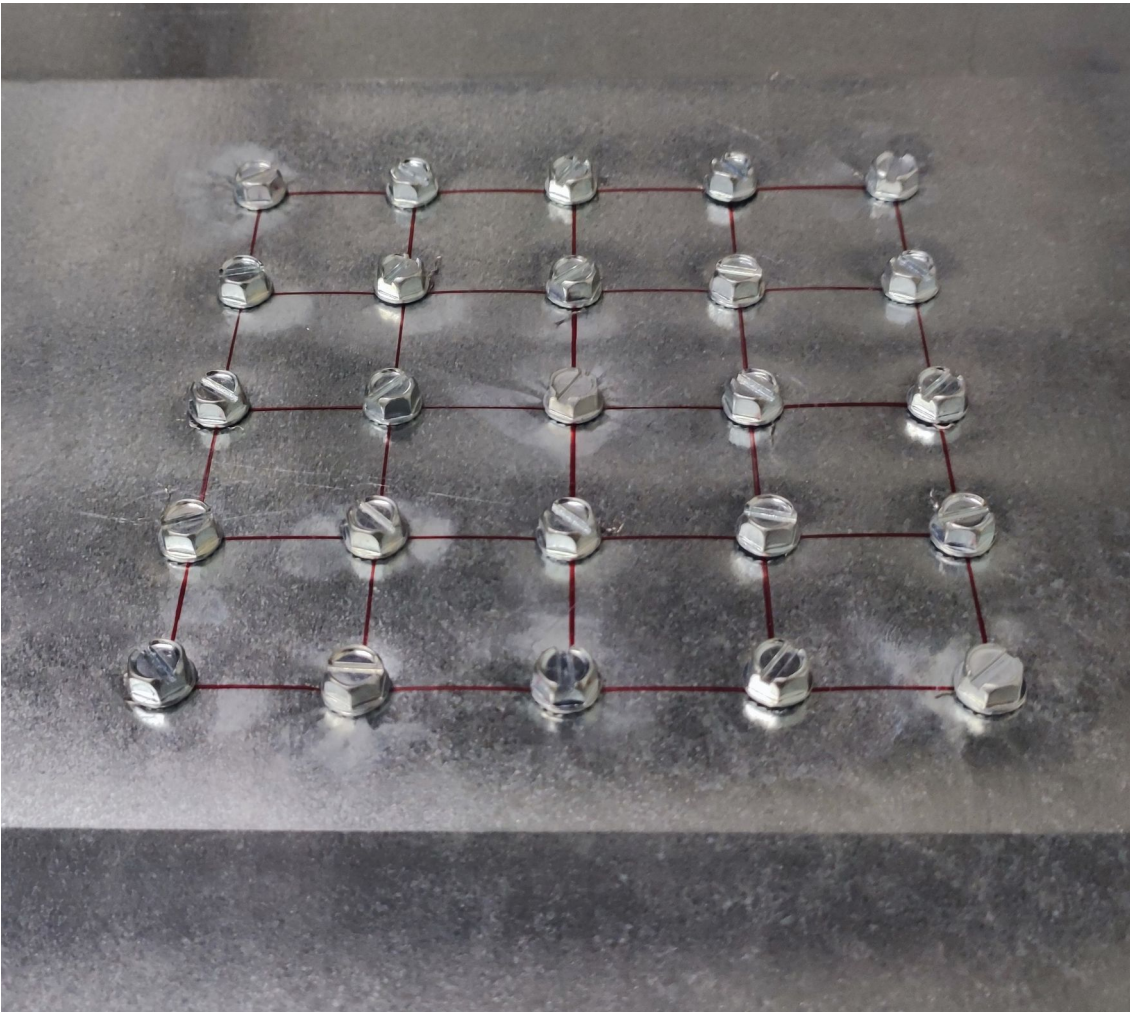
Raster mit 25 eingebrachten Schrauben
